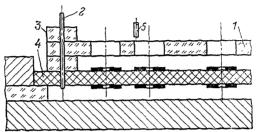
Приспособление для изготовления печатных плат с двусторонним фольгированием.
